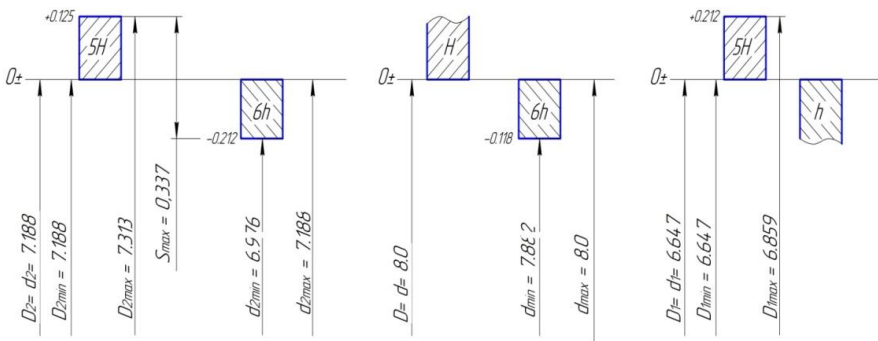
Схеми розташування полів допусків нарізного з'єднання
